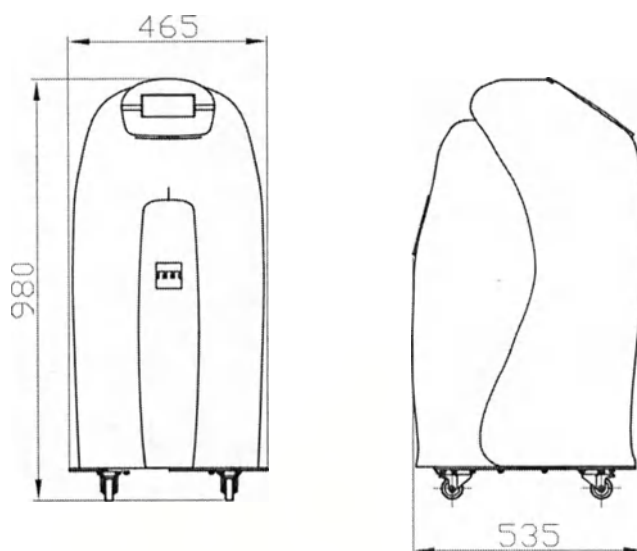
Габаритные размеры генератора установки исполнения Люкс
